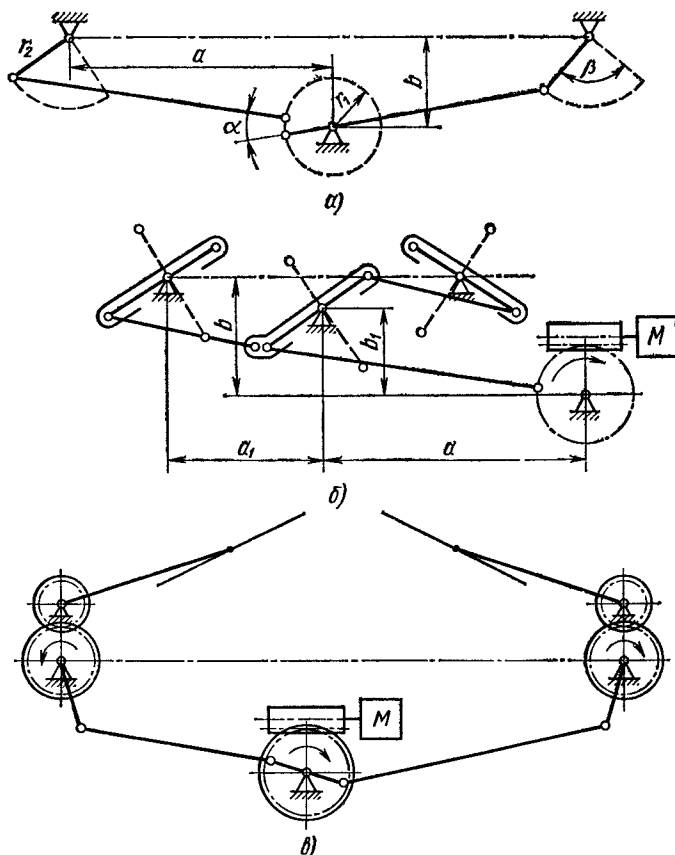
Кинематические схемы кривошипных механизмов для движения щеток:
